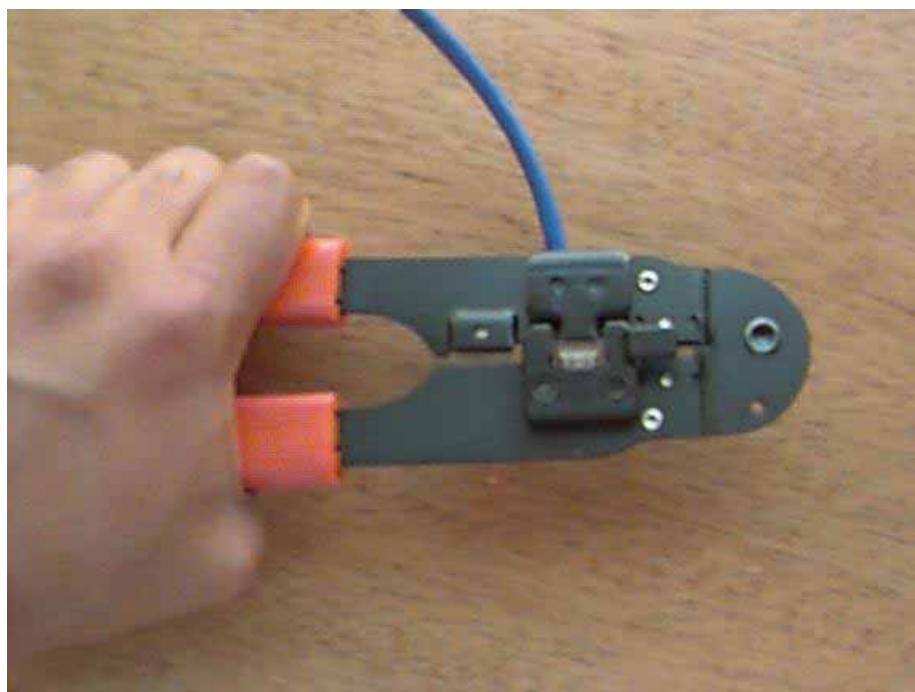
Grimpagem do cabo UTP com conector RJ-45 [2].
